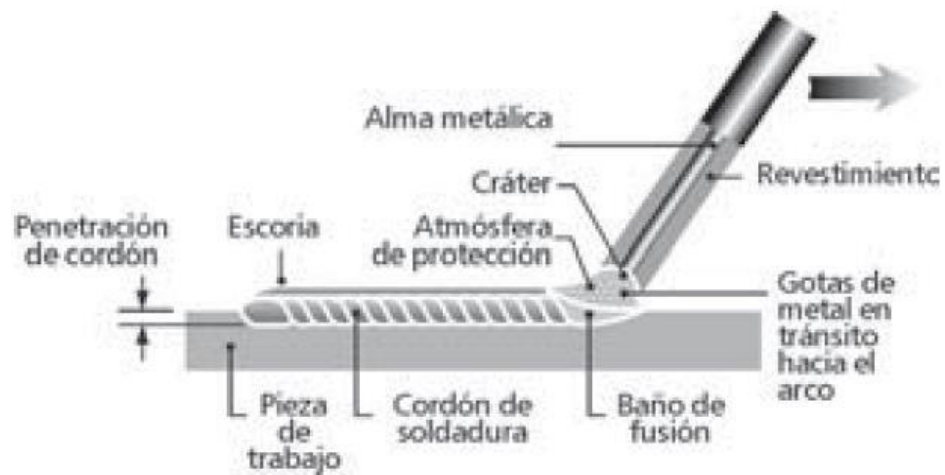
Proceso de soldadura por arco eléctrico. Fuente: Manual de soldadura OERLIKON.
